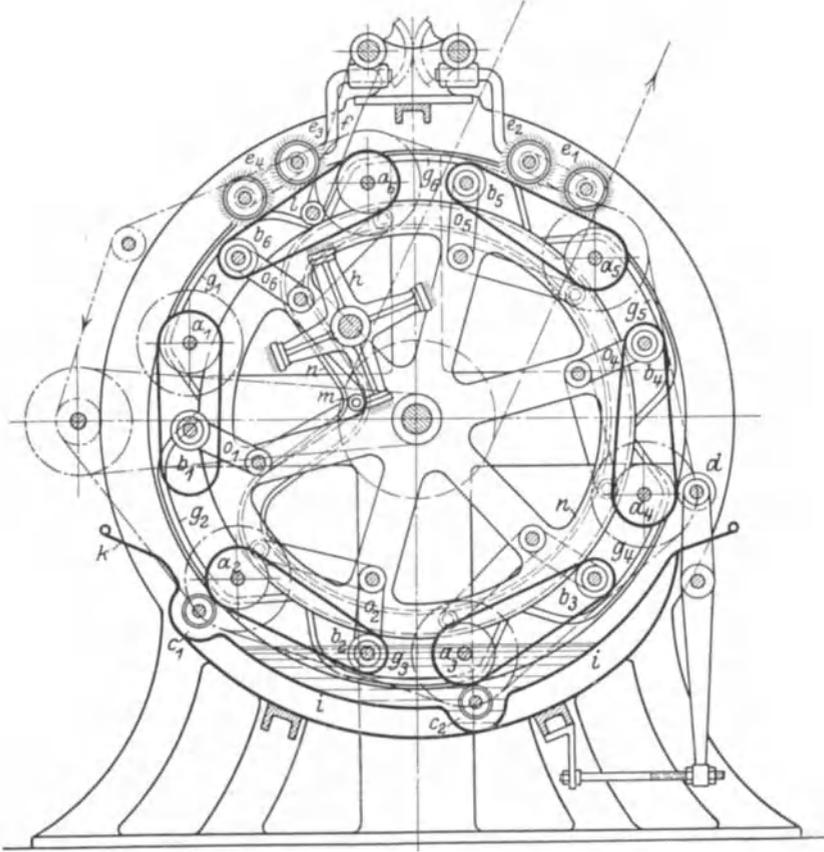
Revolver-Schlichtmaschine für Strähngarn; Textilmaschinenfabrik B. Cohnen G. m. b. H., Grevenbroich b. Köln.
